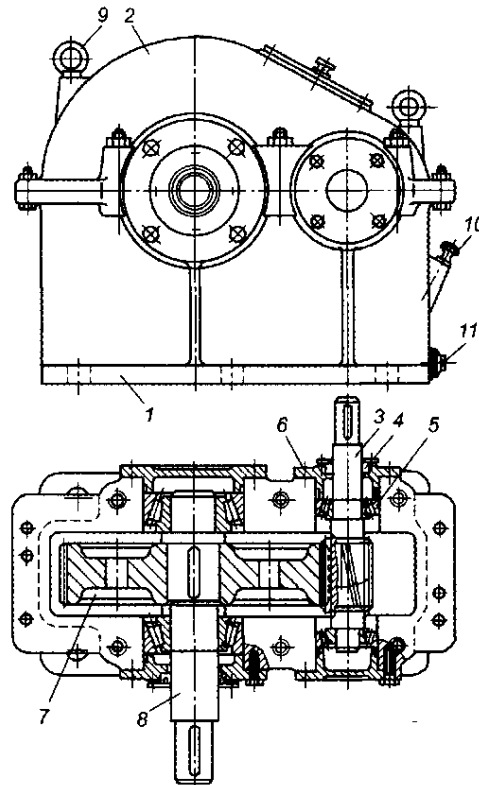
Одноступенчатый редуктор с цилиндрическими косозубыми колесами: 1 — основание корпуса; 2 — крышка корпуса; 3 — ведущий вал-шестерня; 4 — уплотнение; 5 — роликоподшипник конический; 6 — крышка торцовая; 7 — колесо; 8 — вал ведомый; 9 — рым-болт; 10 — жезловый маслоуказатель; 11 — пробка маслоспускная
